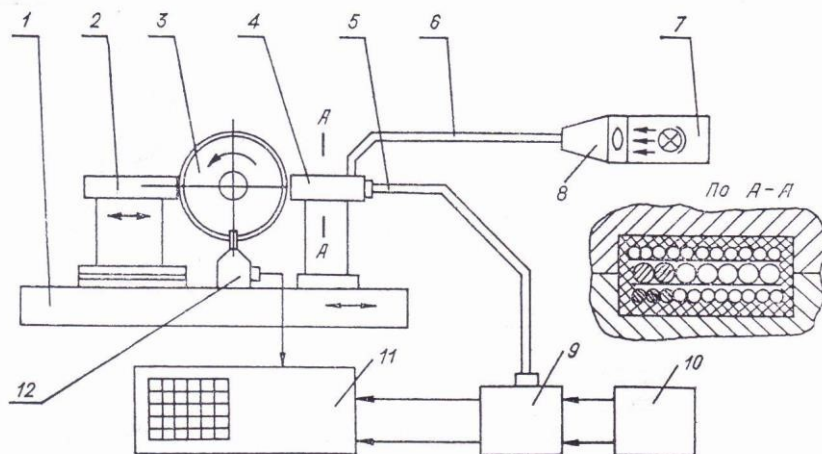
Схема устройства с использованием волоконной оптики: 1 – стол станка; 2 – заготовка; 3 – алмазный круг; 4 – образец датчик микро перемещений; 5, 6 – жгуты световодов; 7, 8 – источник и усилитель света; 9, 10 – ФЭУ и источник его питания; 11, 12 – осциллограф и прерыватель для его запуска
